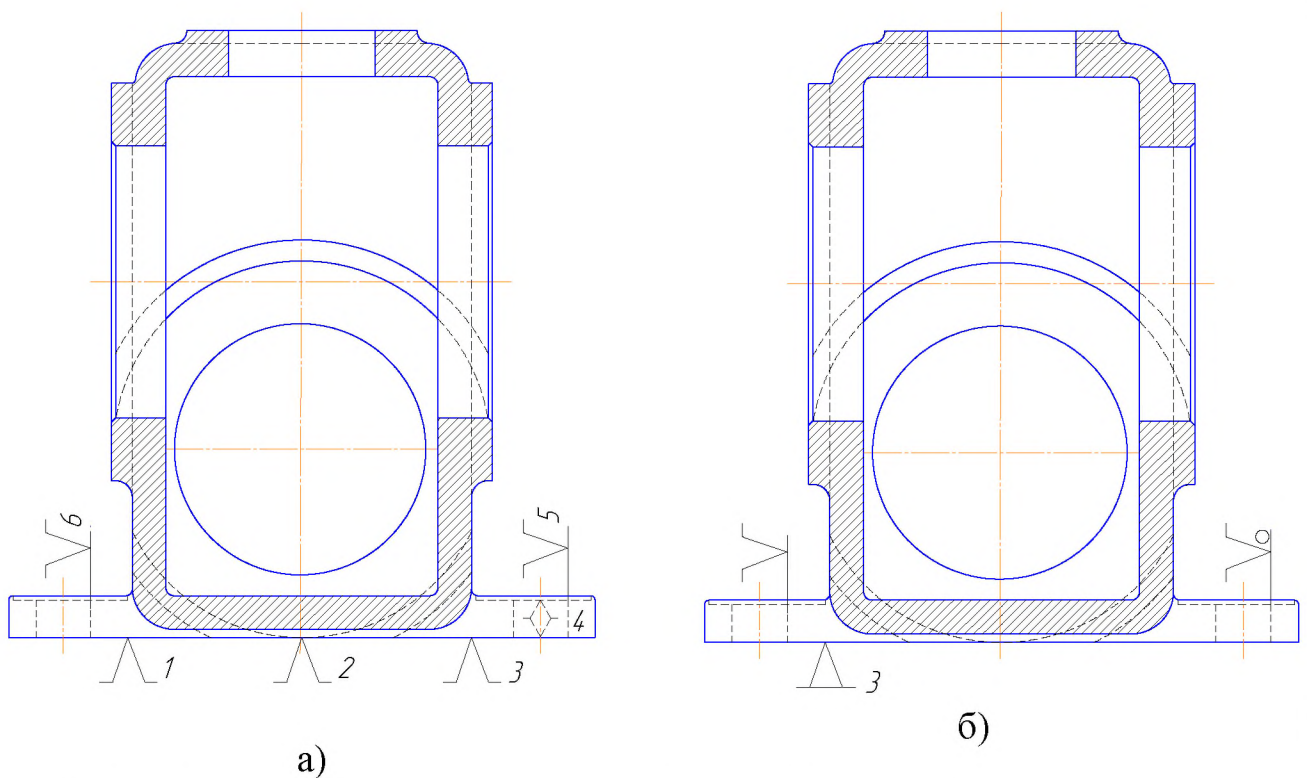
Схема базування корпусу: а) теоретична; б) умовна
